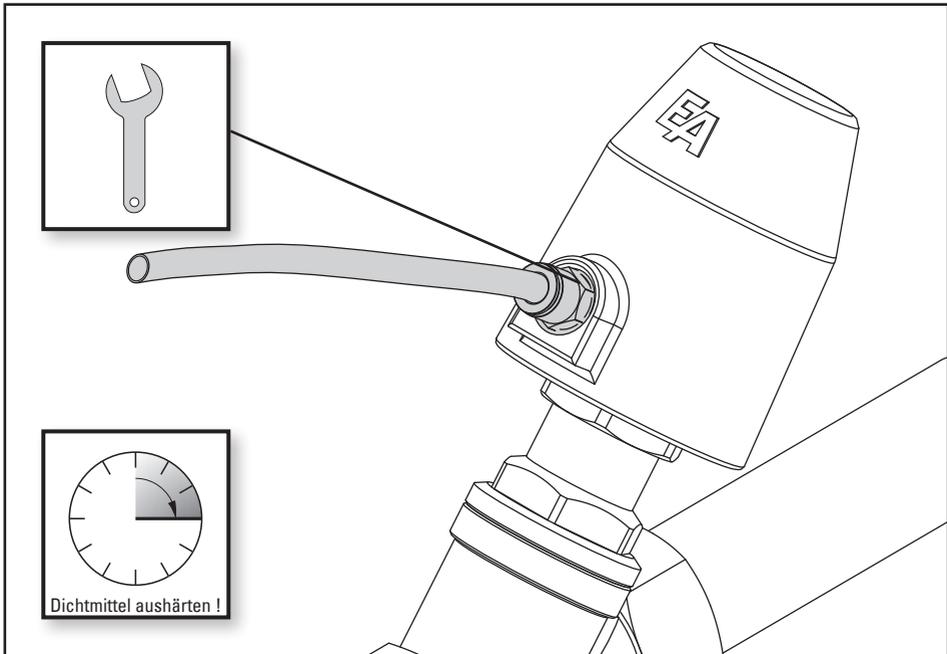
Montage / Demontage - Anschluss Steuermedium
